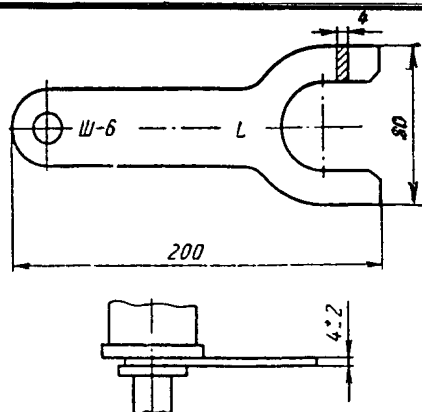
Шаблон Ш-6 для контроля зазора механизма поворота замедлителя КВ
